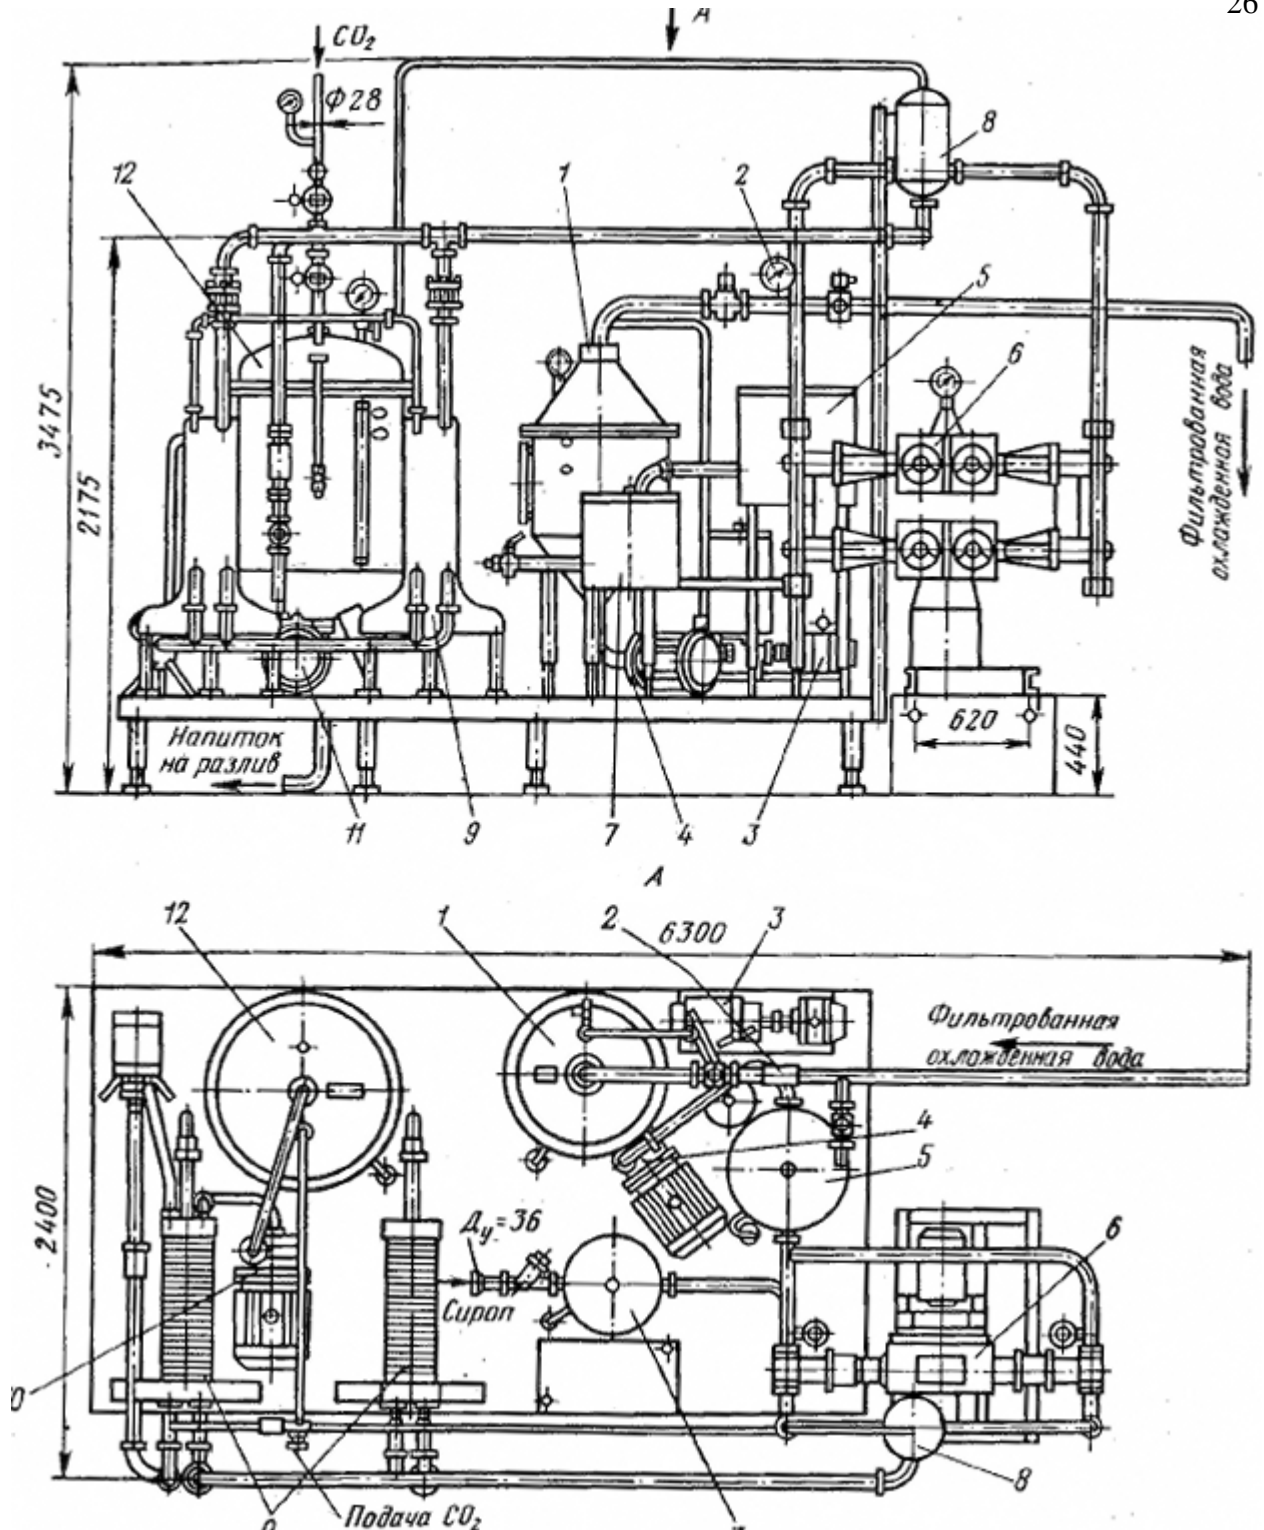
Схема установки Б2-ВРР/6 для приготовления газированных напитков
